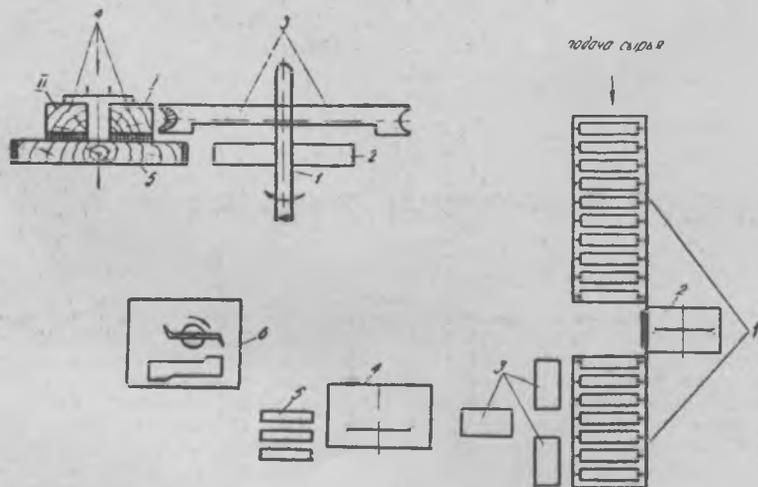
и 4. Схема обработки заготовок и поточной линии для производства топорниц.
